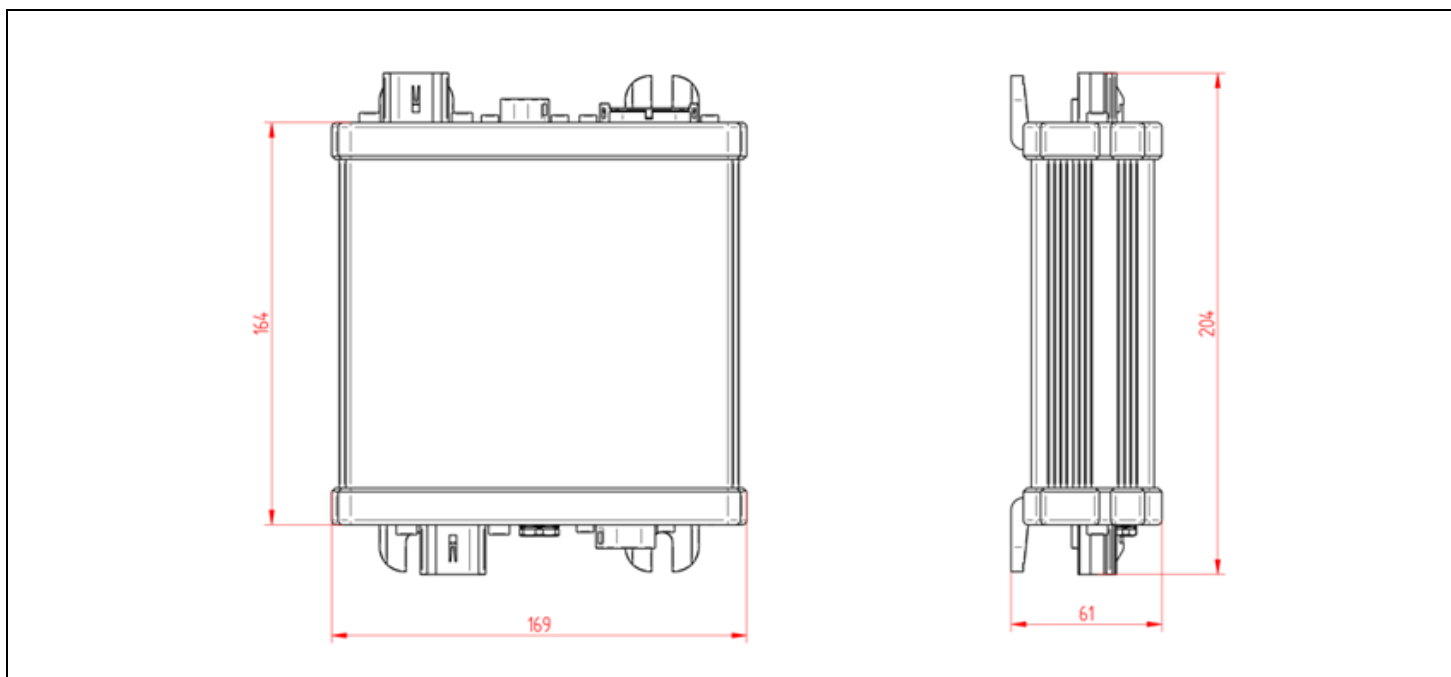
Механические размеры: ECU ДВИГАТЕЛЬ
